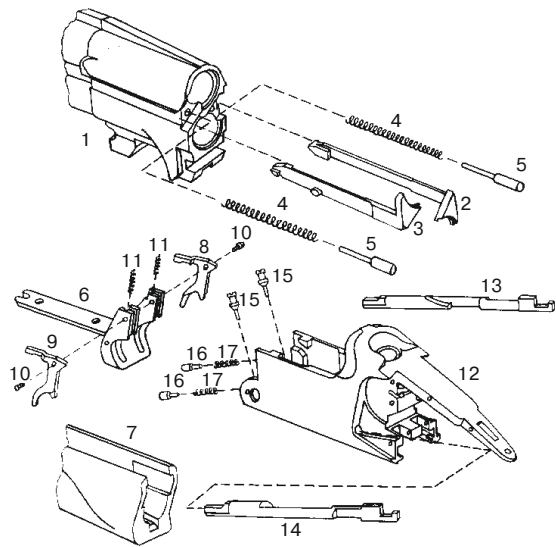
Детали ружья ИЖ-27ЕМ
